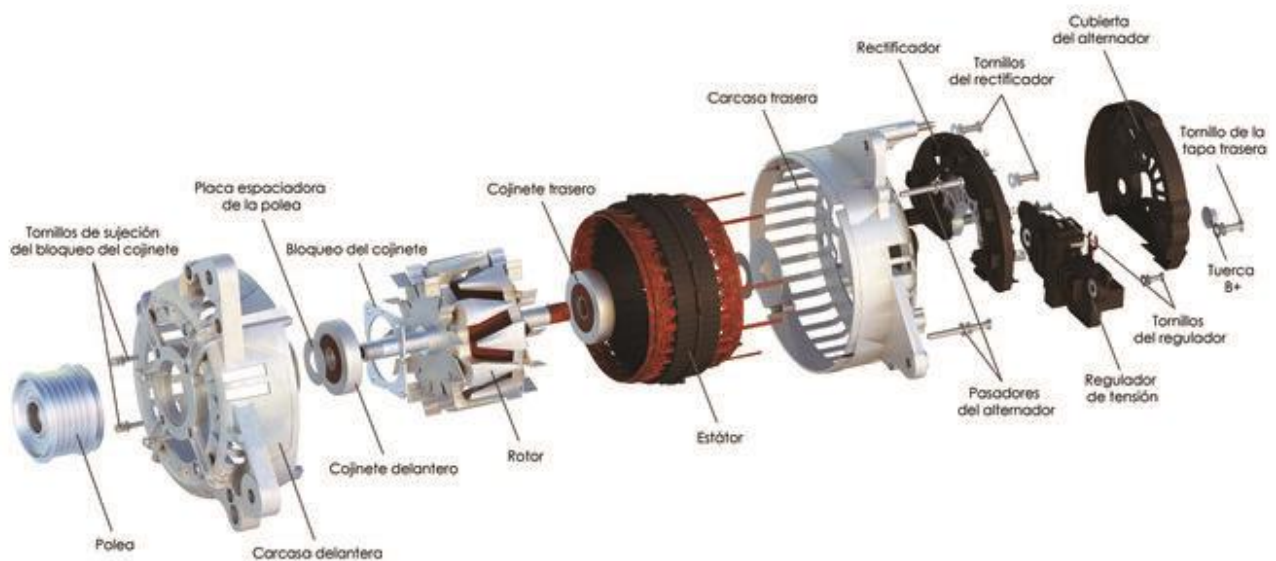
Partes de un alternador (fuente: infotaller) [3]
